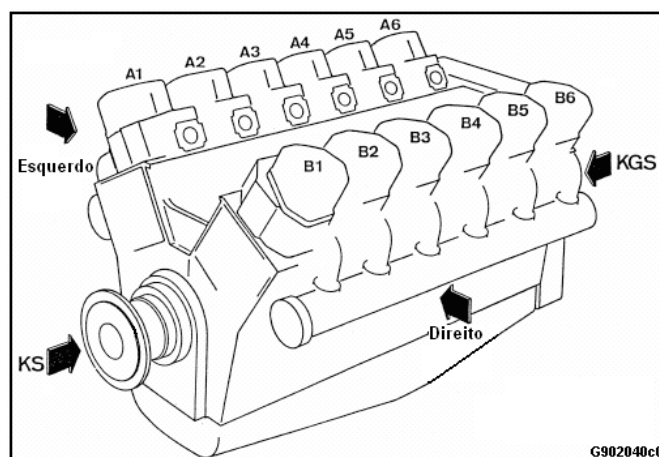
Representação do motor MTU (MTU Friedrichshfen, 1993)
